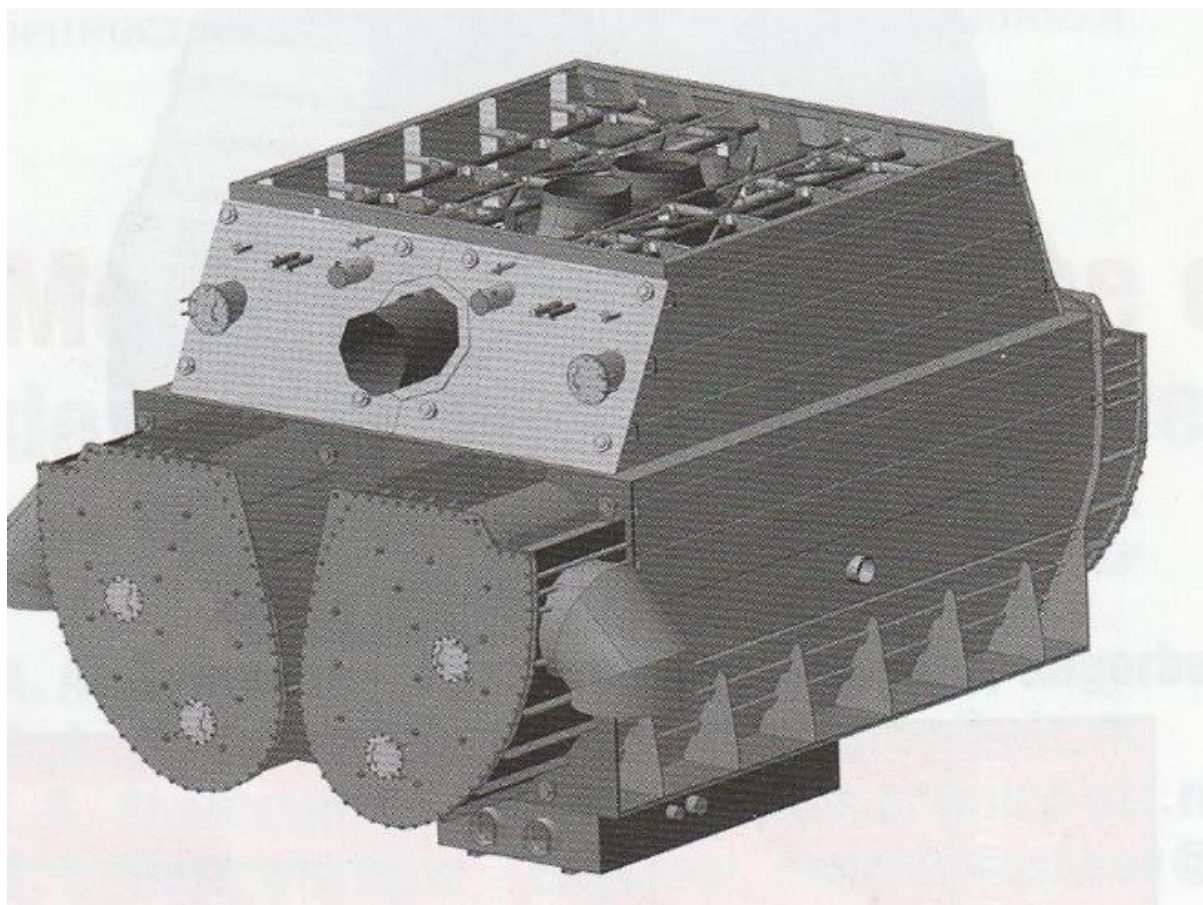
Общий вид конденсатора К-9500 [2]
